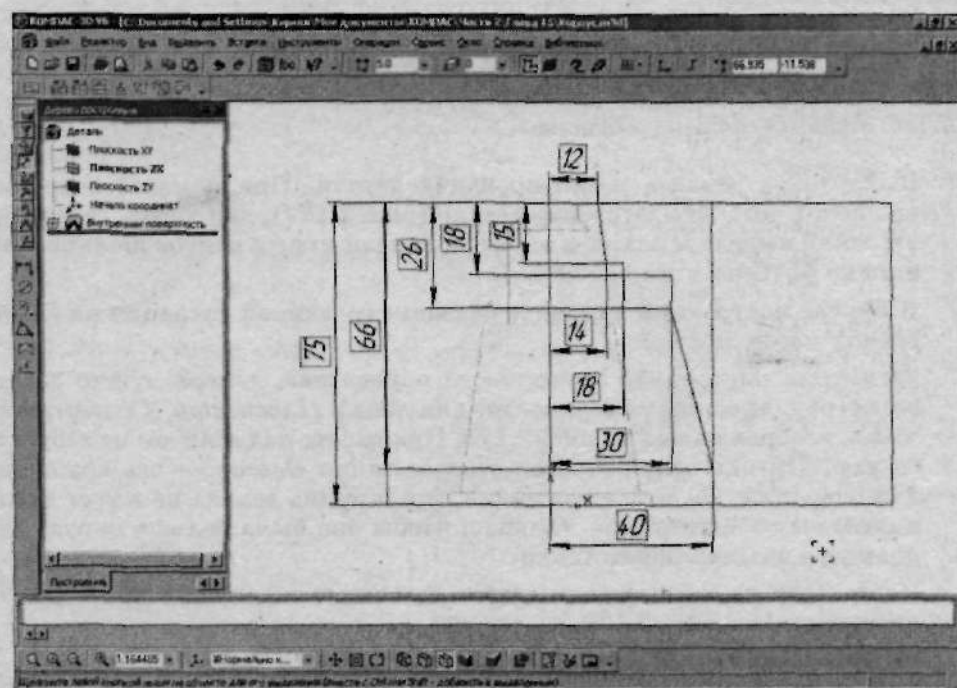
Для того чтобы определить вид наружной поверхности детали, создайте эскиз
